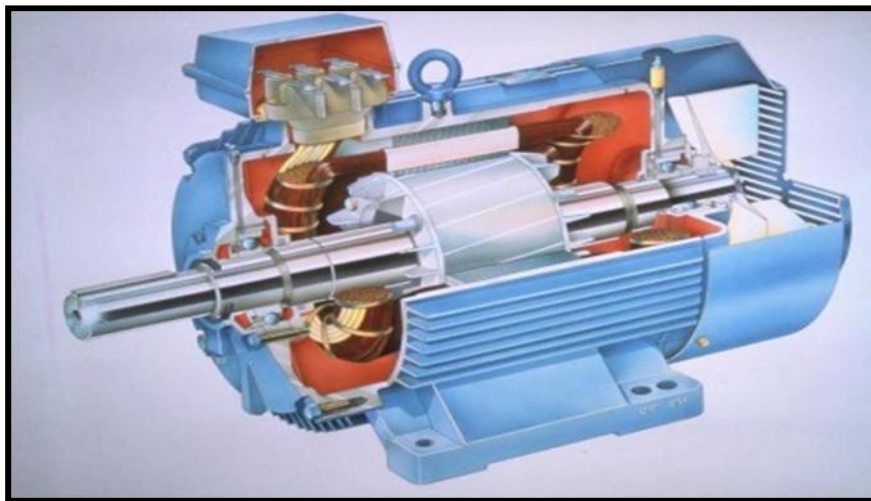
Machine asynchrone avec rotor à cage d'écureuil
